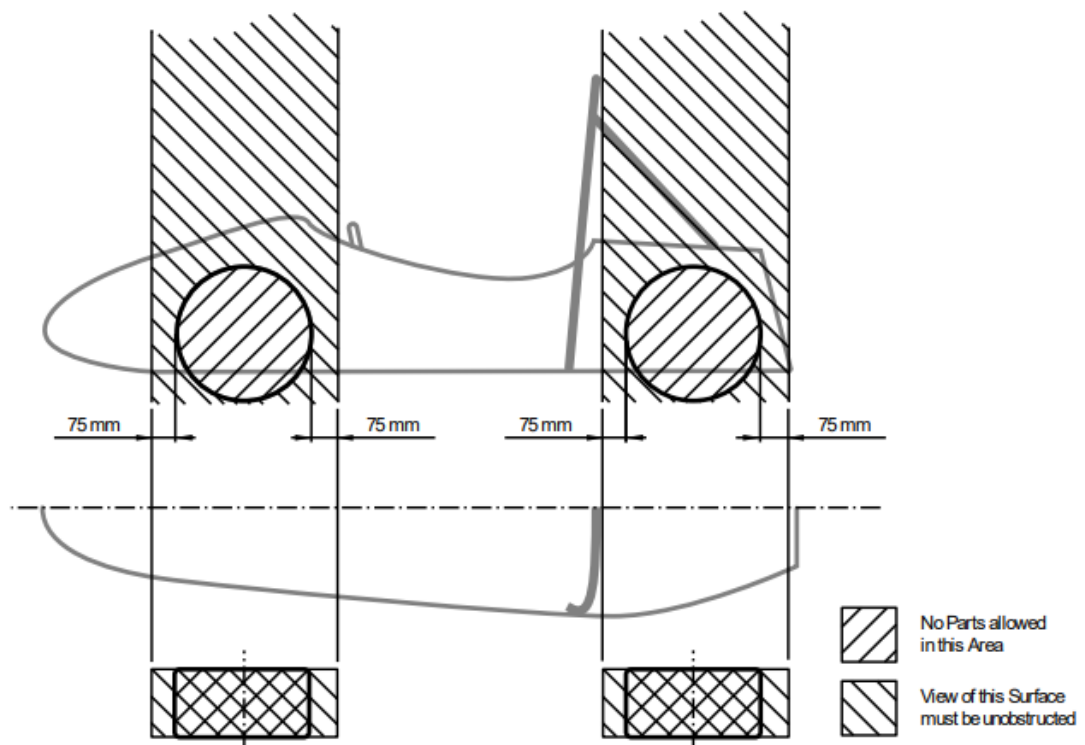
Keep out zone e superfícies que devem ser visíveis.
